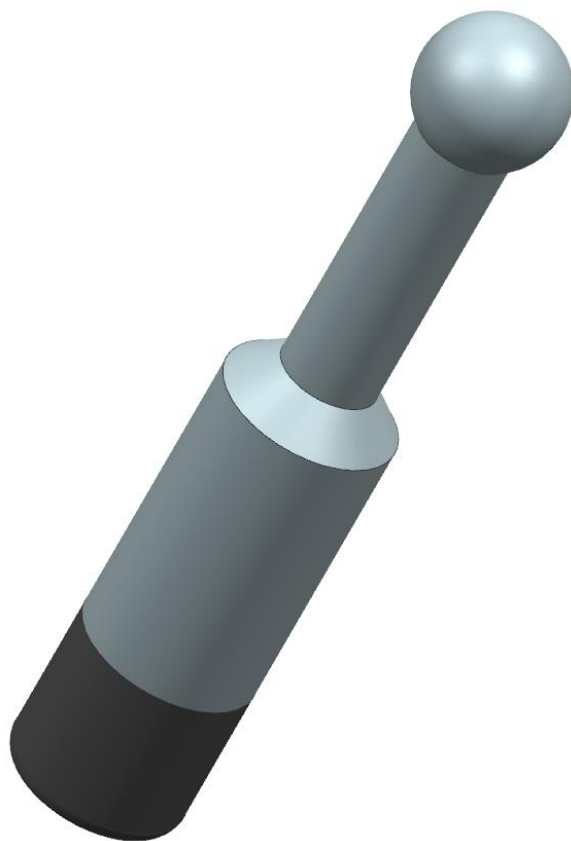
5-Ф-98, Оправка для установки поршневой группы в блок цилиндров
